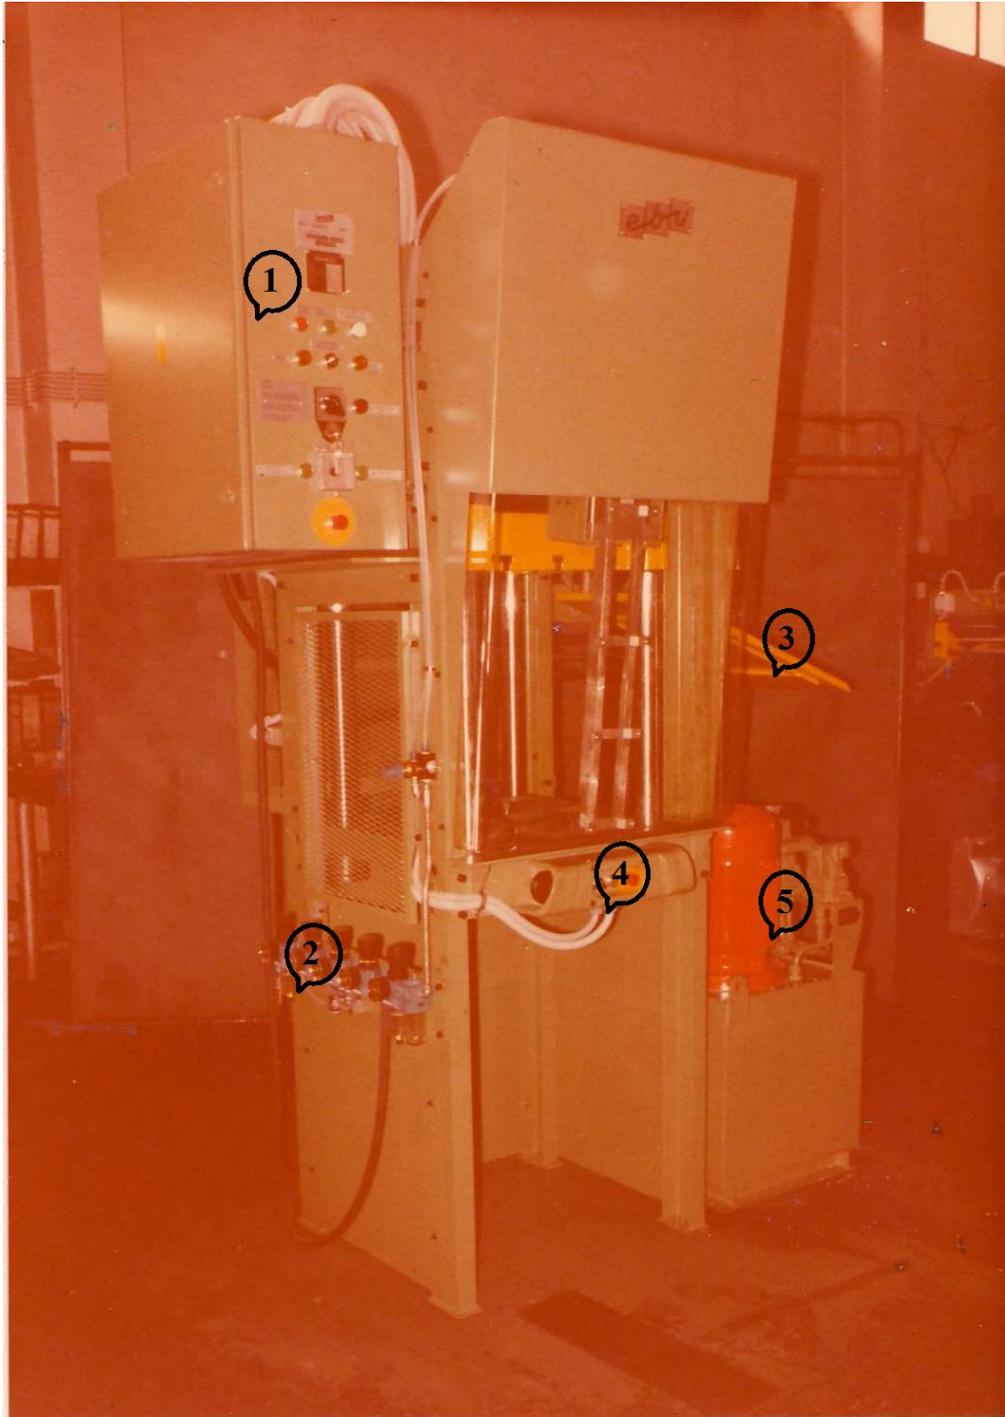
Vue réelle de la presse hydraulique à ébavurer.
